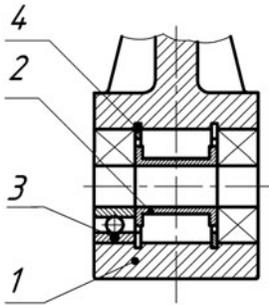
Схема установки подшипников при сквозной расточке с разжимными стопорными кольцами
